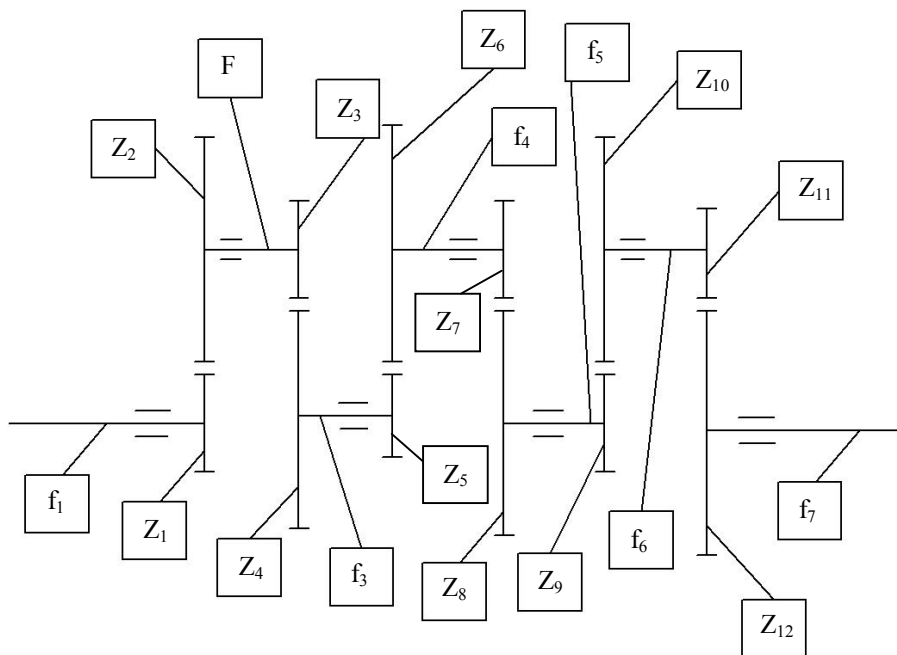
Кинематическая схема мотора редуктора РД-09
